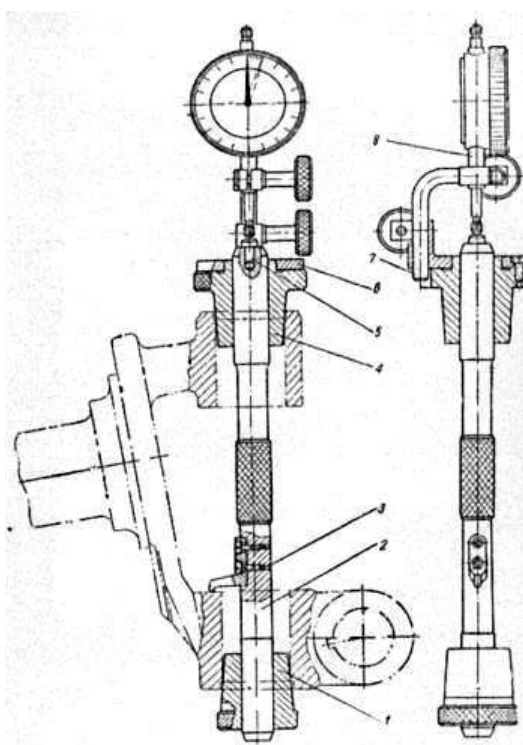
Пристрій для перевірки перпендикулярності торців до осі поворотного кулака: 1, 4 – втулки; 2 – валик; 3 – упор; 5 – опора; 6 – кронштейн; 7 – державка; 8 – індикатор
